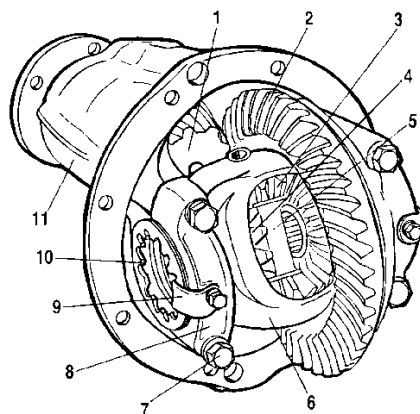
Составляющие редуктора: 1 – ведущая шестерня; 2 – ведомая шестерня; 3 – сателлит; 4 – шестерня полуоси; 5 – ось сателлитов; 6 – коробка дифференциала; 7 – болты крепления крышки подшипника коробки дифференциала; 8 – крышка подшипника коробки дифференциала; 9 – стопорная пластина; 10 – регулировочная гайка подшипника; 11 – картер редуктора.
